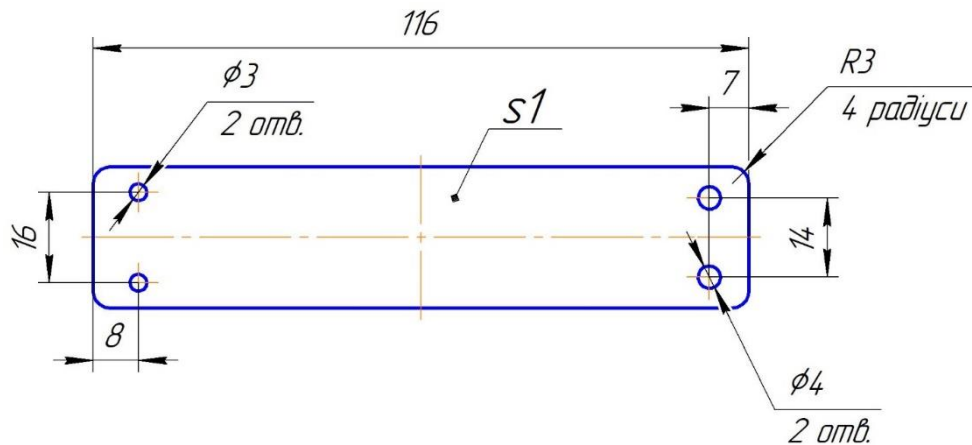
Ескіз заготовки для деталі «кронштейн фіксуєчий».
